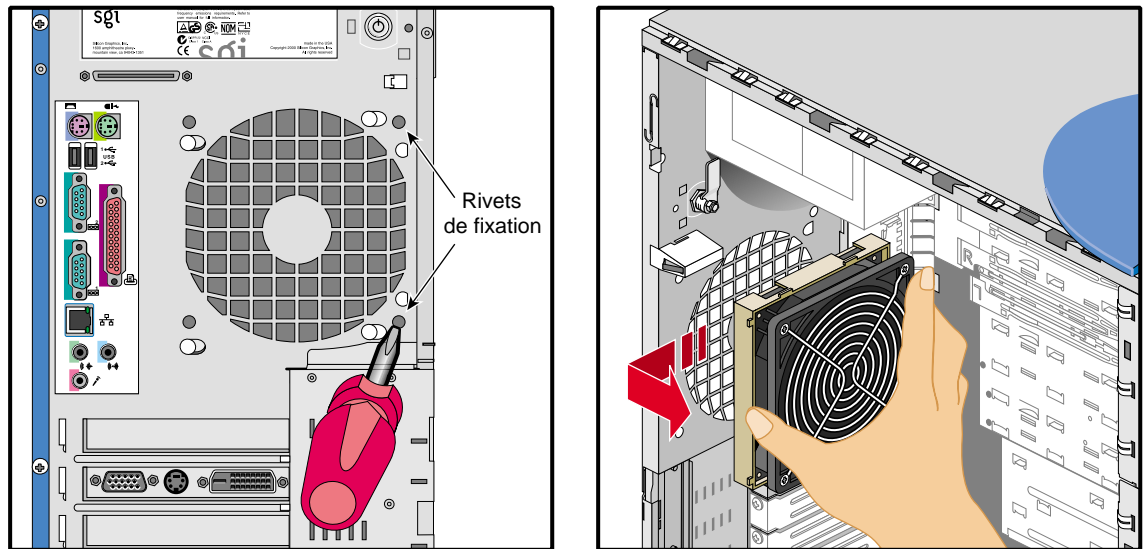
Décliquetage des rivets de fixation et démontage du ventilateur arrière
